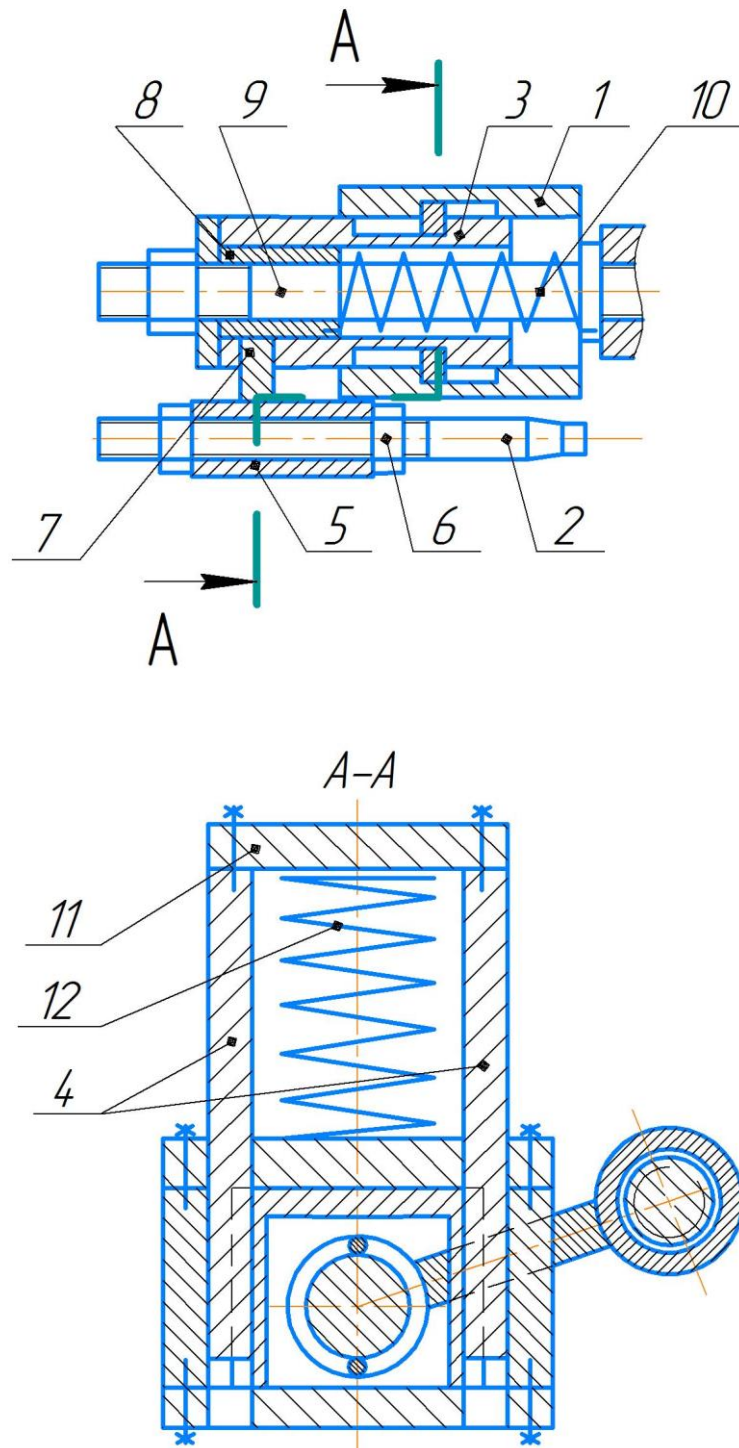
Механізм упору до штампу для відрізки сортового прокату зсувом
